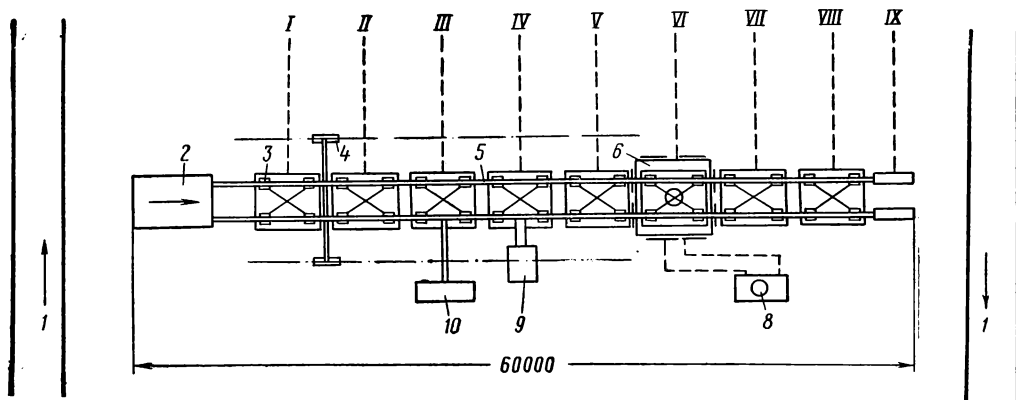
Схема конвейера для ремонта и сборки тележек электропоездов:
